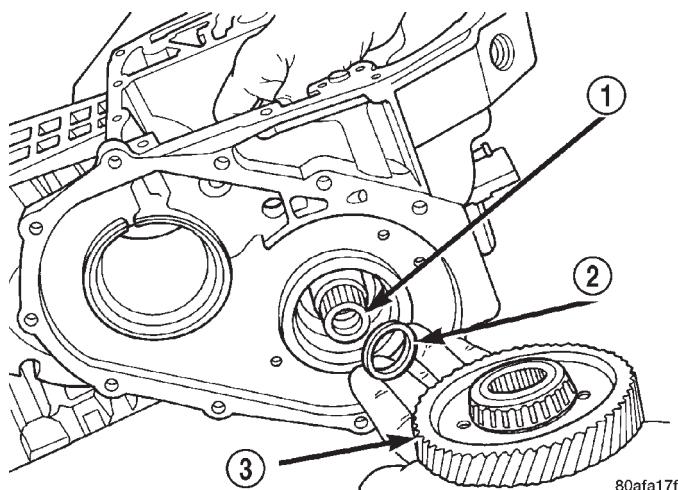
Engranaje transmisor y espaciador (selectivo)
